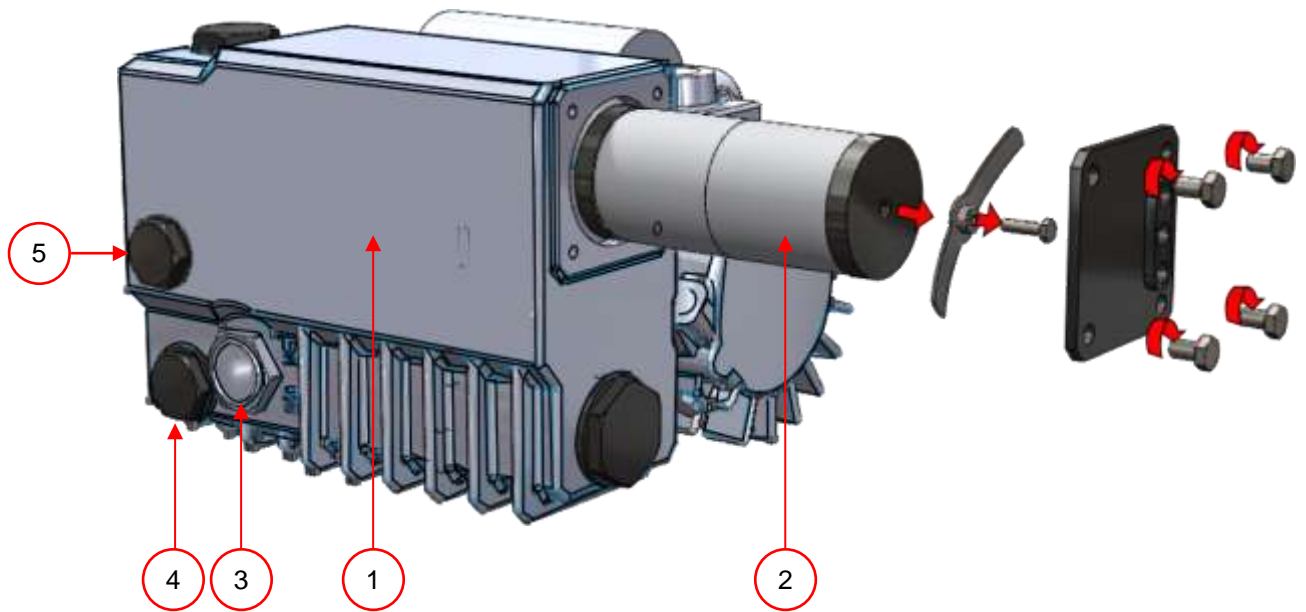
Vue d'ensemble des pompes (couvercle du filtre enlevé)
